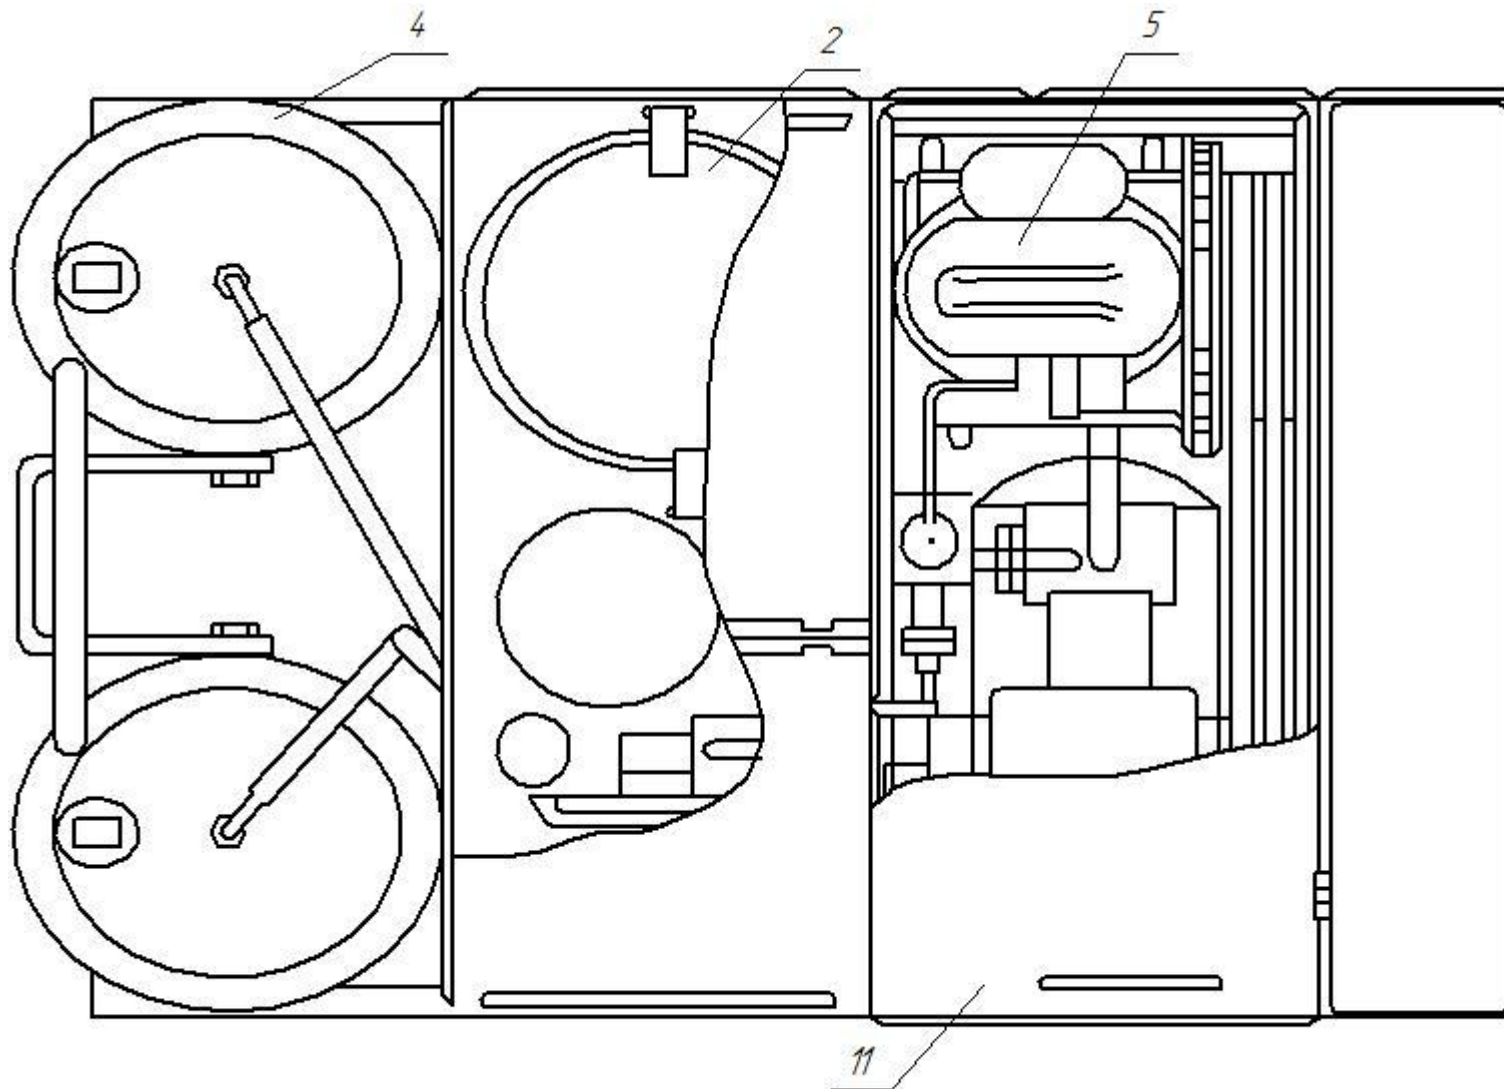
б Установка для подготовки техники к хранению ОЗ-9995-ГОСНИТИ (вид сверху)
